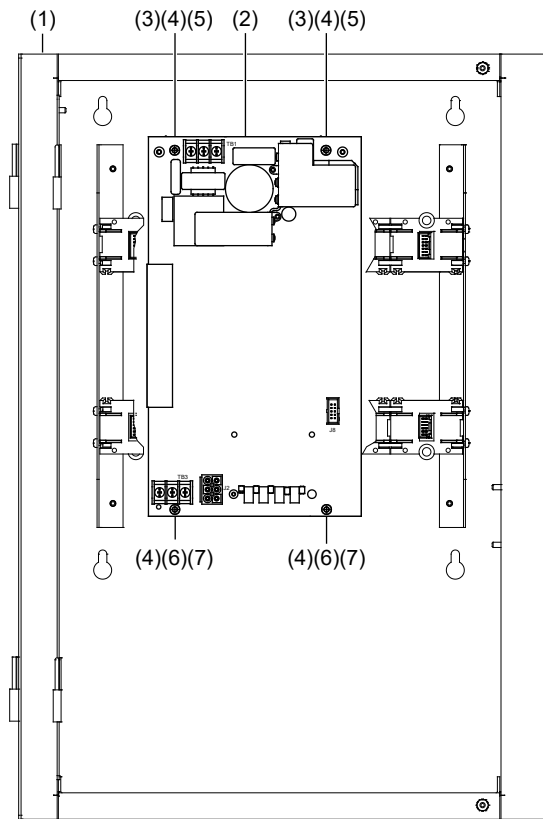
Instalação da placa principal PSU em um chassi 3-CHAS7
